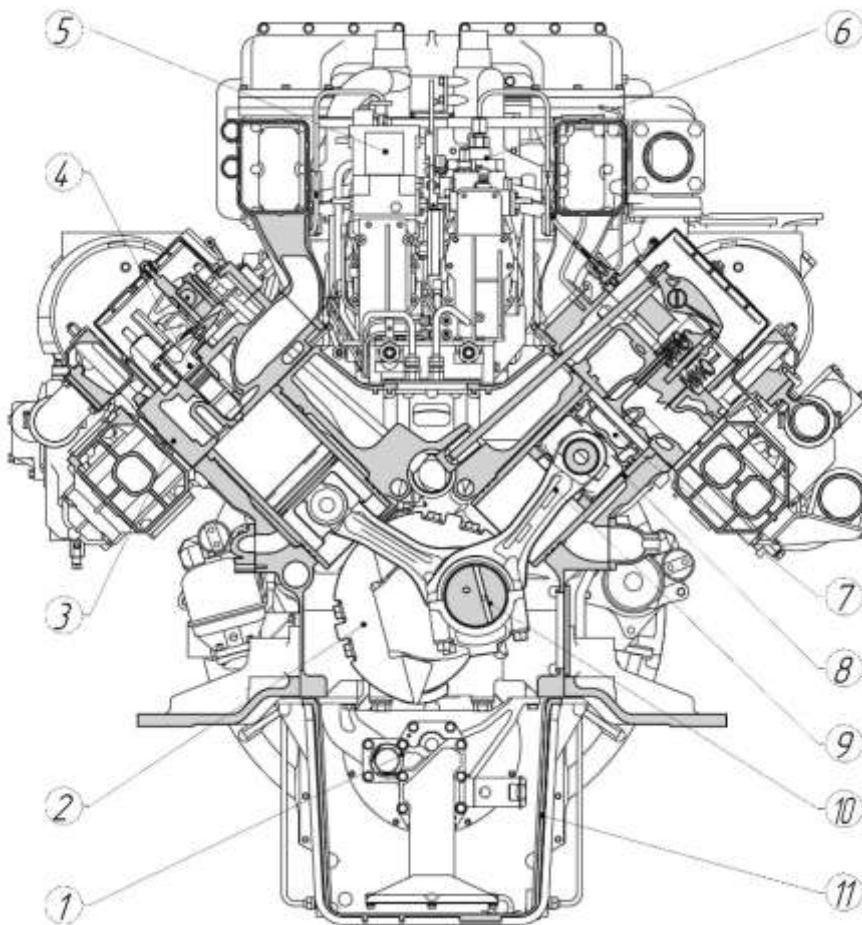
Високообертовий двигун Yanmar 12AUM-WGT: 1 – насос масляний; 2 – противага колінчастого валу; 3 – кришка циліндра; 4 – паливна форсунка; 5 – регулятор гідравлічний; 6 – ПНВТ; 7 – поршень; 8 – циліндрова втулка; 9 – шатун; 10 – вал колінчастий; 11 – піддон масляний
